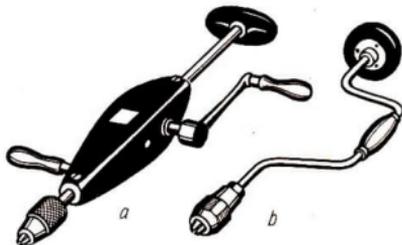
/4 a Handbohrmaschine, b Bohrwinde
